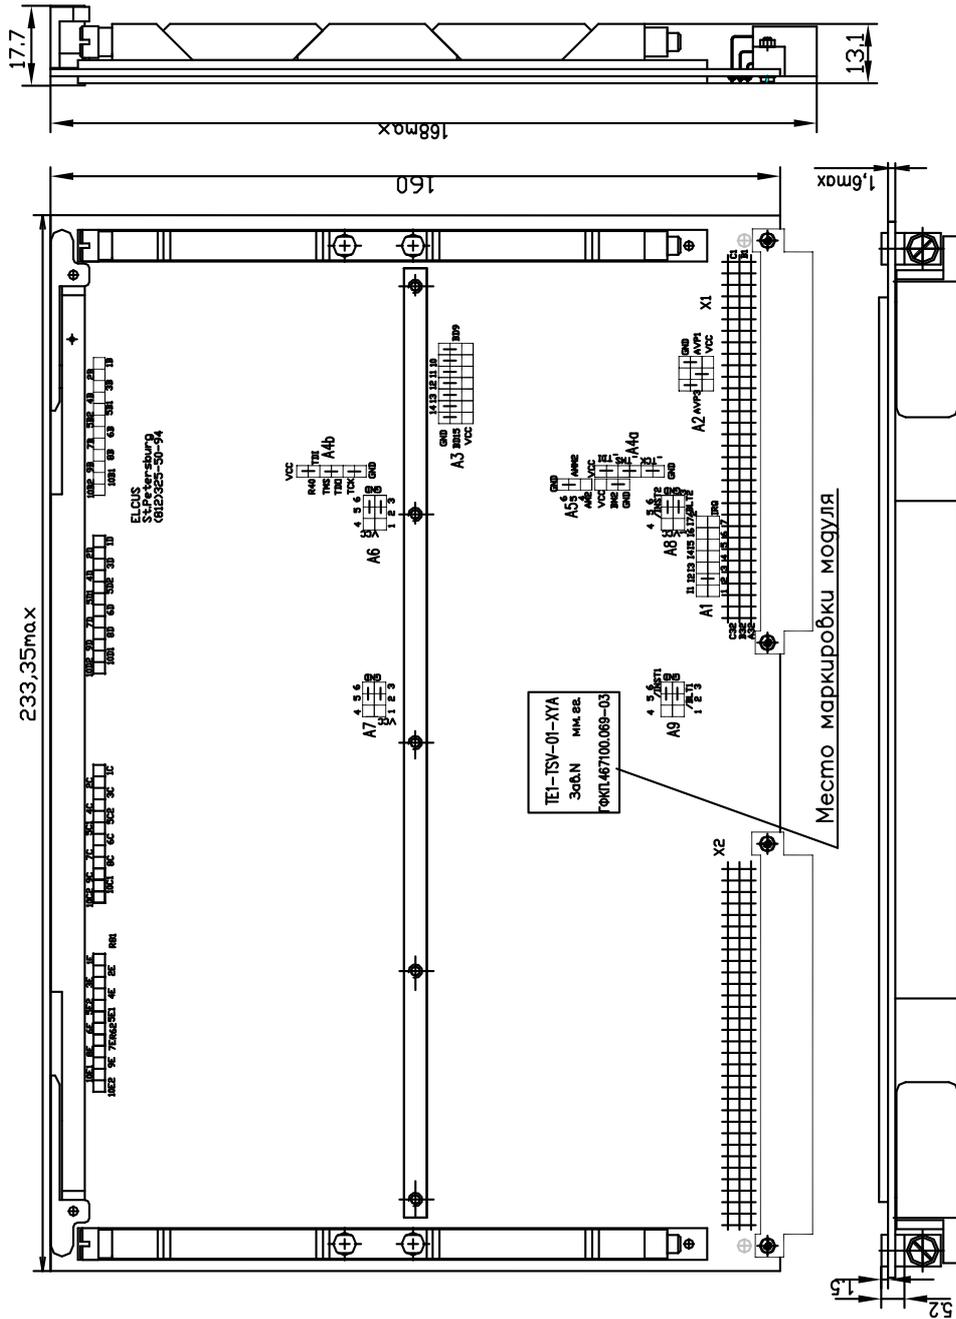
Габаритный чертеж модуля TE1-TSV-01-4R
